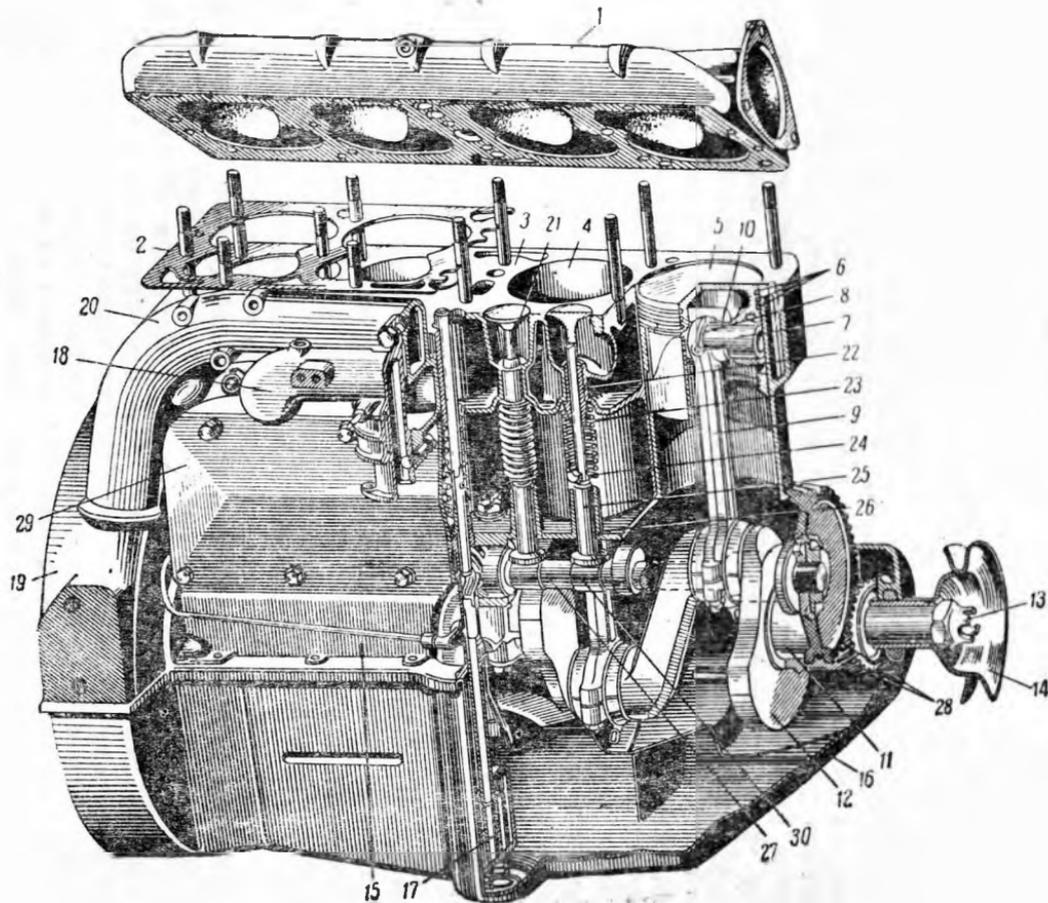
Продольный разрез двигателя ГАЗ-МК:
